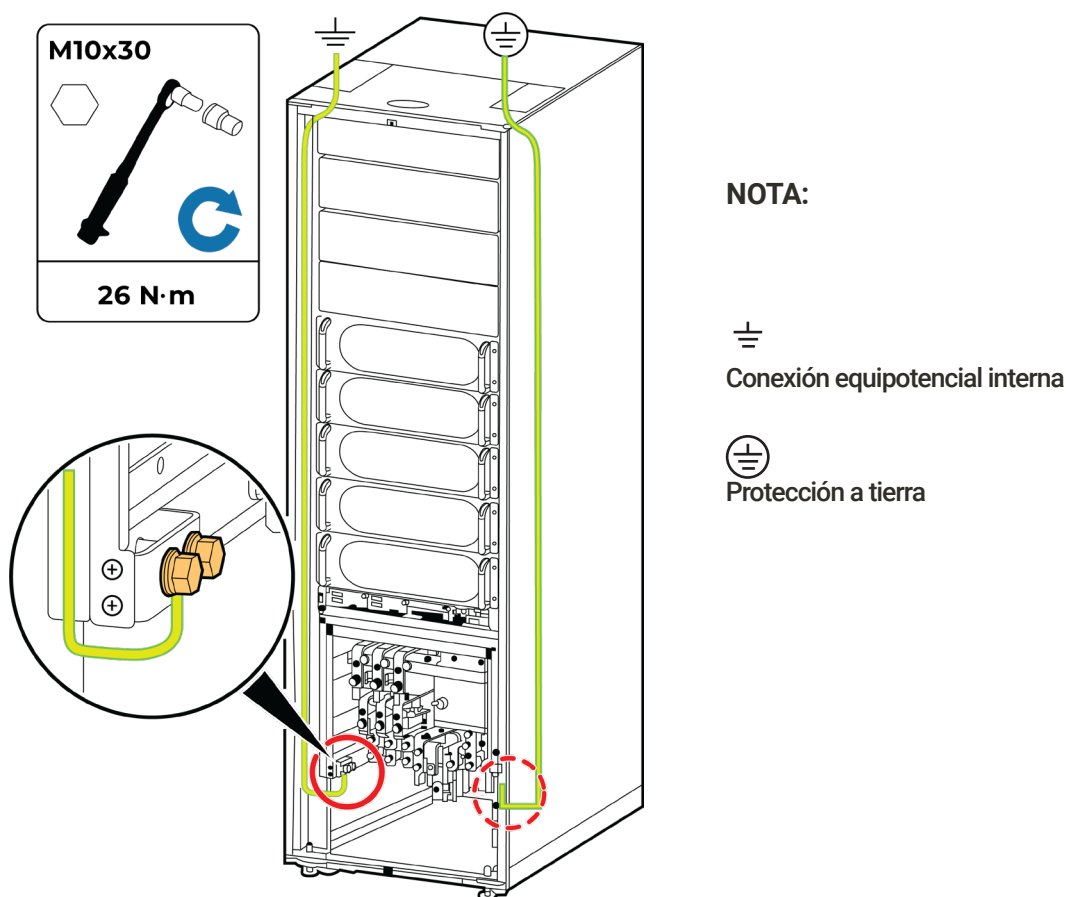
CABLEADO DE PROTECCIÓN A TIERRA
